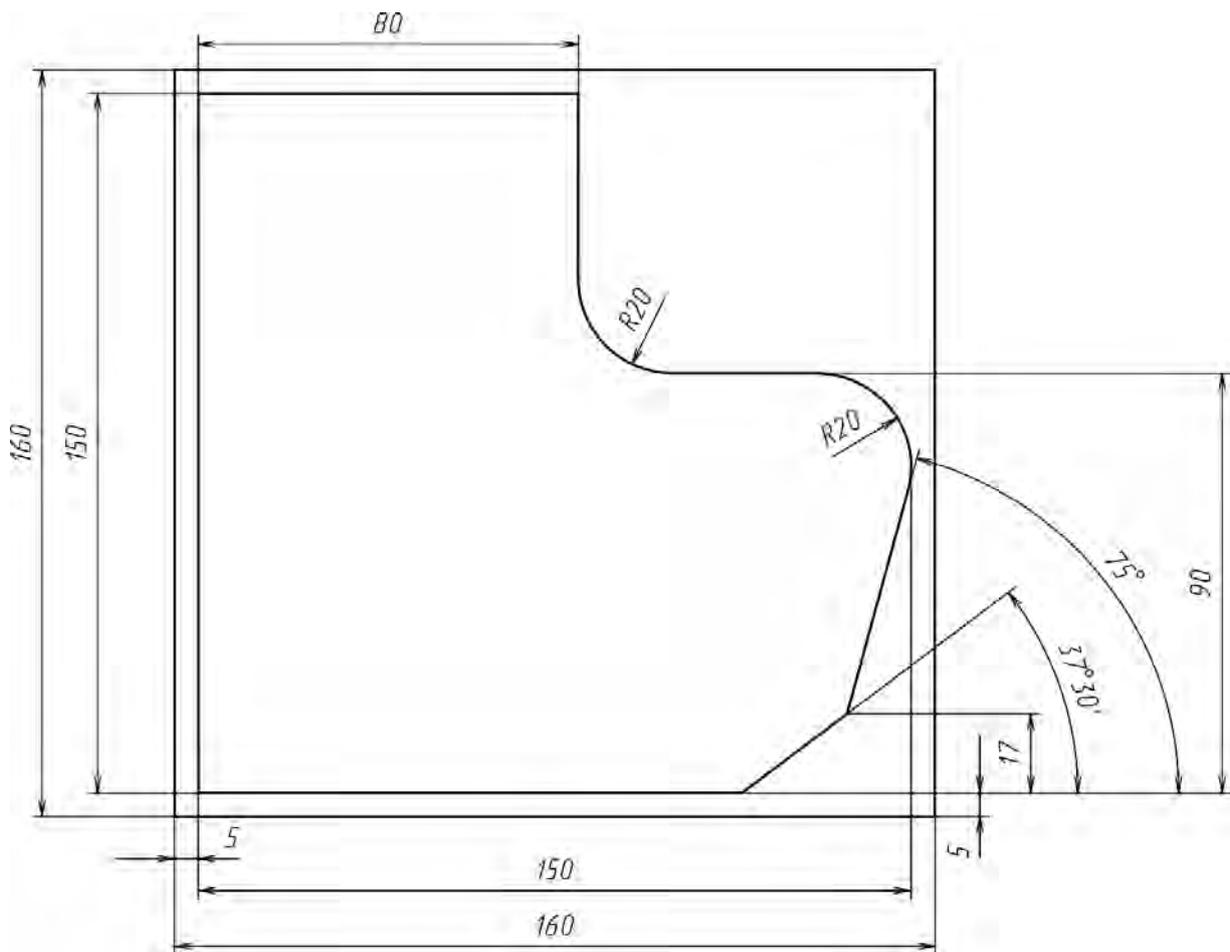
Эскиз обрабатываемой заготовки
